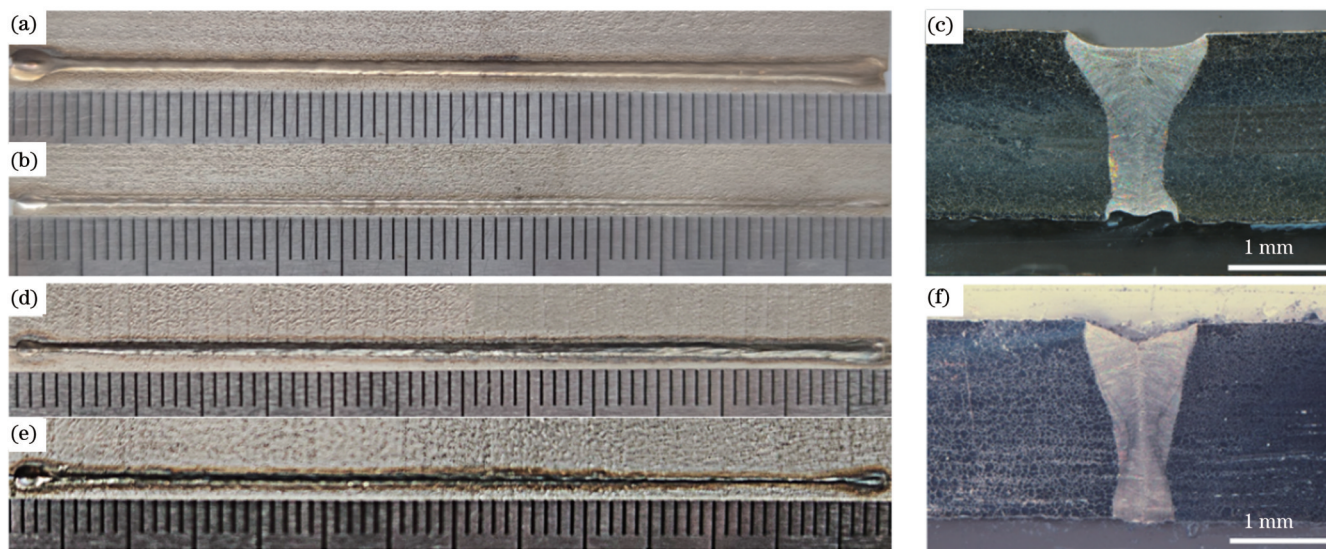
焊缝的外观和横截面。陆上焊接焊缝的(a)正面,(b)背面,(c)截面;水下焊接焊缝的(d)正面,(e)背面,(f)截面
